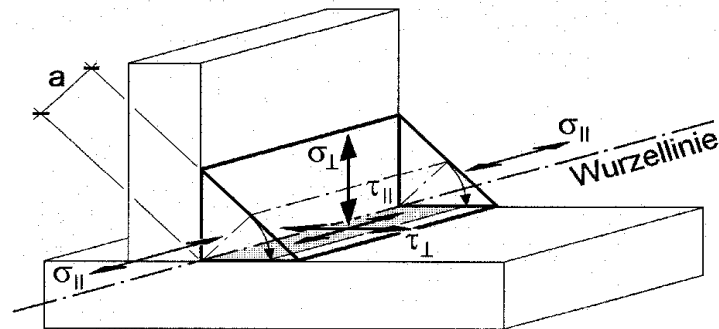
Schweißnahtspannungen in der Anschlussebene einer Kehlnaht nach (10) Seite 298
